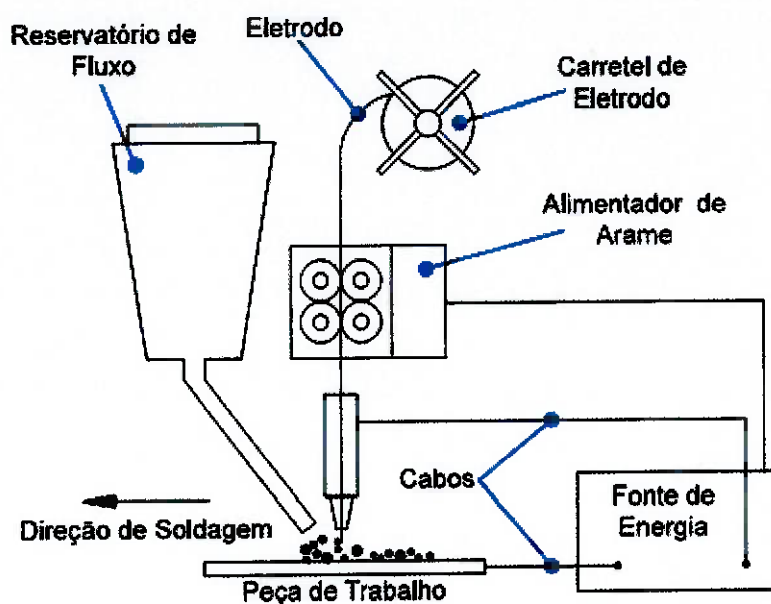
Esquema do equipamento da soldagem por arco submerso [3].
